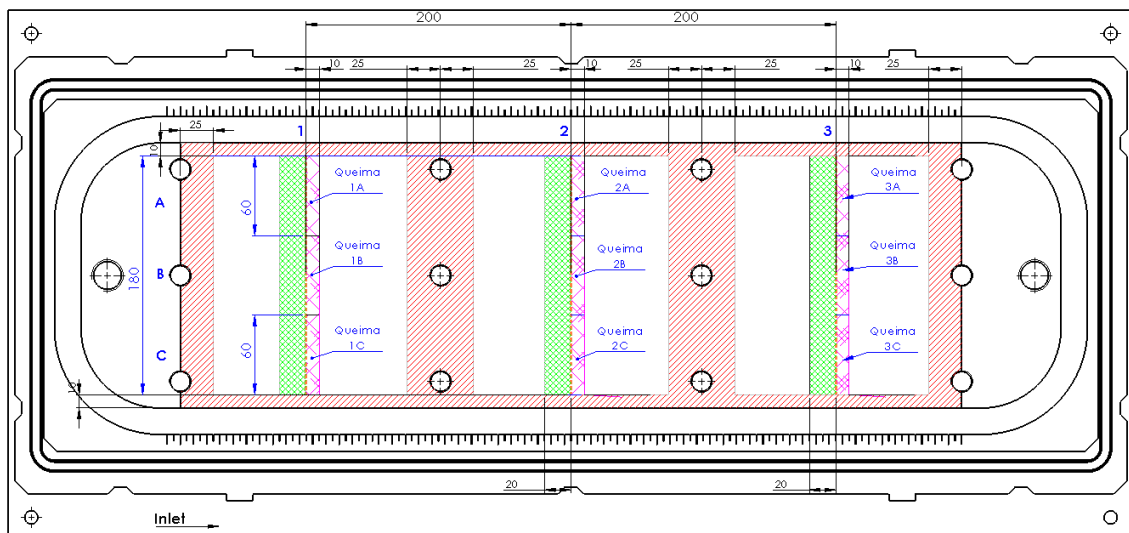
Localização e plano de corte das amostras de queima.
